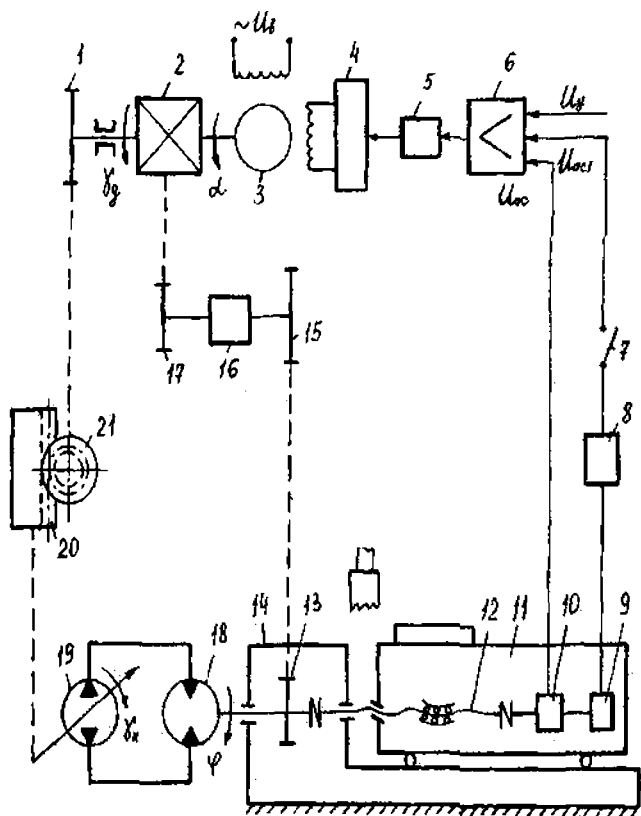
Принципиальная схема электрогидравлического привода с машинным управлением фрезерного станка
